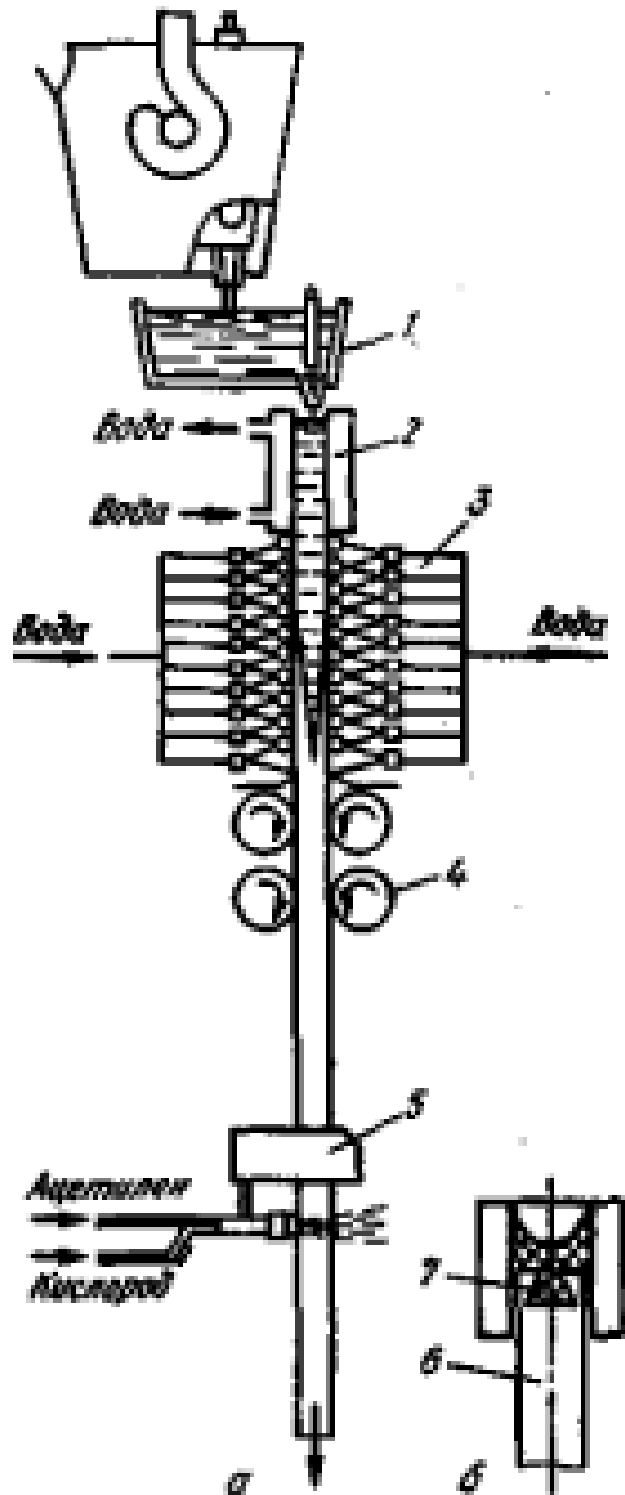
Схемы разливки стали на МНЛЗ (а) и действия затравки (б):
